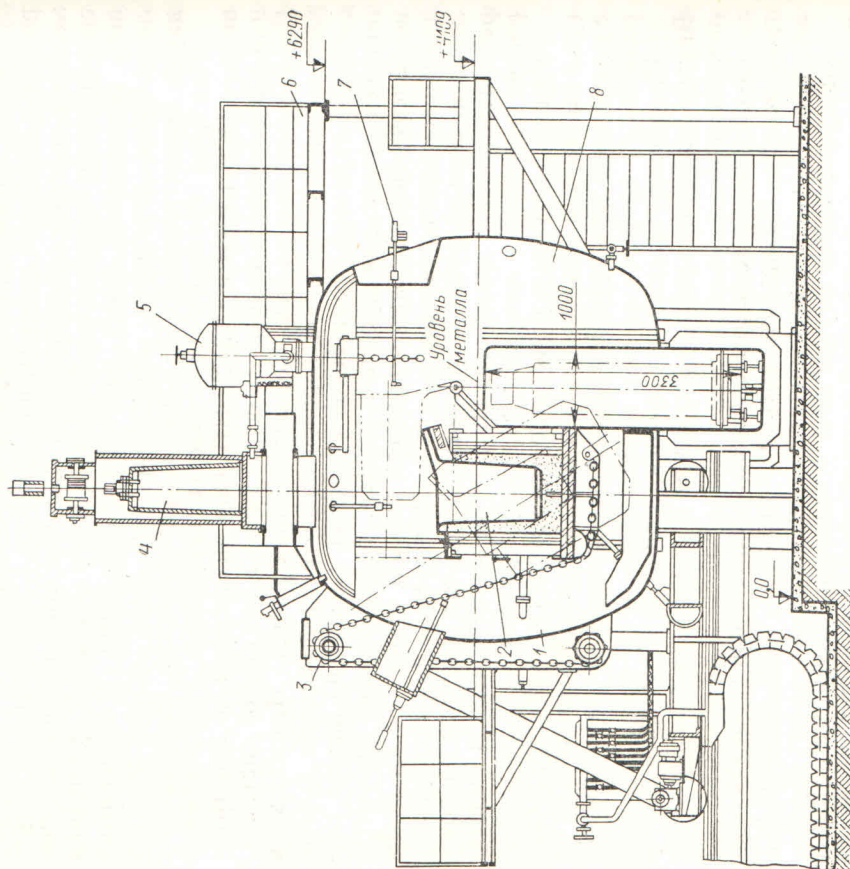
Проект 2,5-т вакуумной печи: 1 — подвижная часть плавильной камеры; 2 — индукционная печь; 3 — механизм наклона печи; 4 — камера загрузки; 5 — дозатор; 6 — рабочая площадка; 7 — устройство для чистки тигля; 8 — неподвижная часть плавильной камеры
